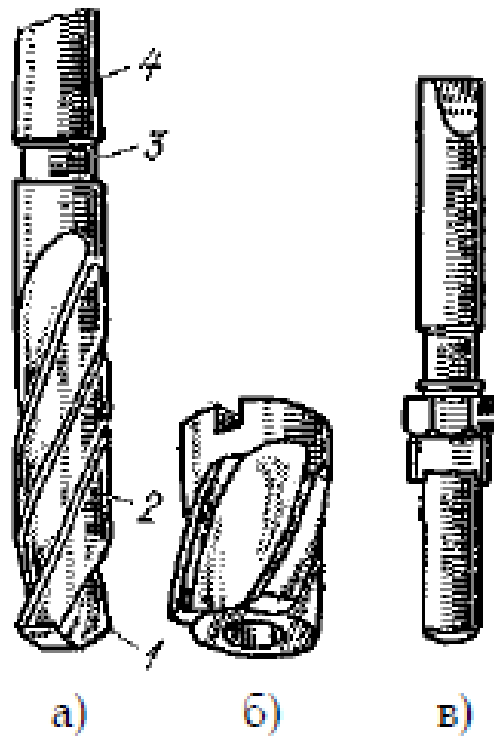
Зенкери: а – циліндричний суцільний (1– ріжучі крайки, 2 – робоча частина, 3 – шийка, 4 – лапка); б – насадний; в – зі вставними ножами
